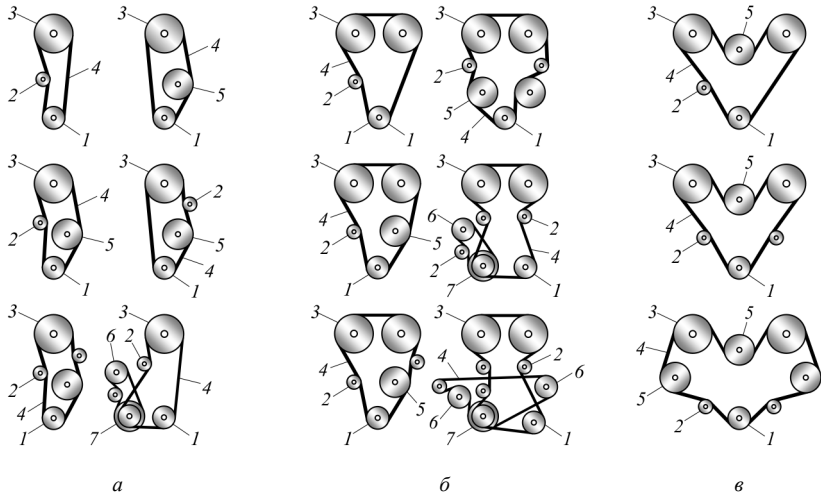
Основные схемы ременного привода механизмов: *а* – двигателя с одним верхним распределительным валом; *б* – двигателя с двумя верхними распределительными валами; *в* – V-образного двигателя с двумя верхними распределительными валами; 1 – шкив коленчатого вала; 2 – натяжные и (или) паразитные ролики; 3 – шкив распределительного вала; 4 – ремень; 5 – шкив вала вспомогательных механизмов; 6 – шкив балансирующего вала; 7 – шкив генератора
